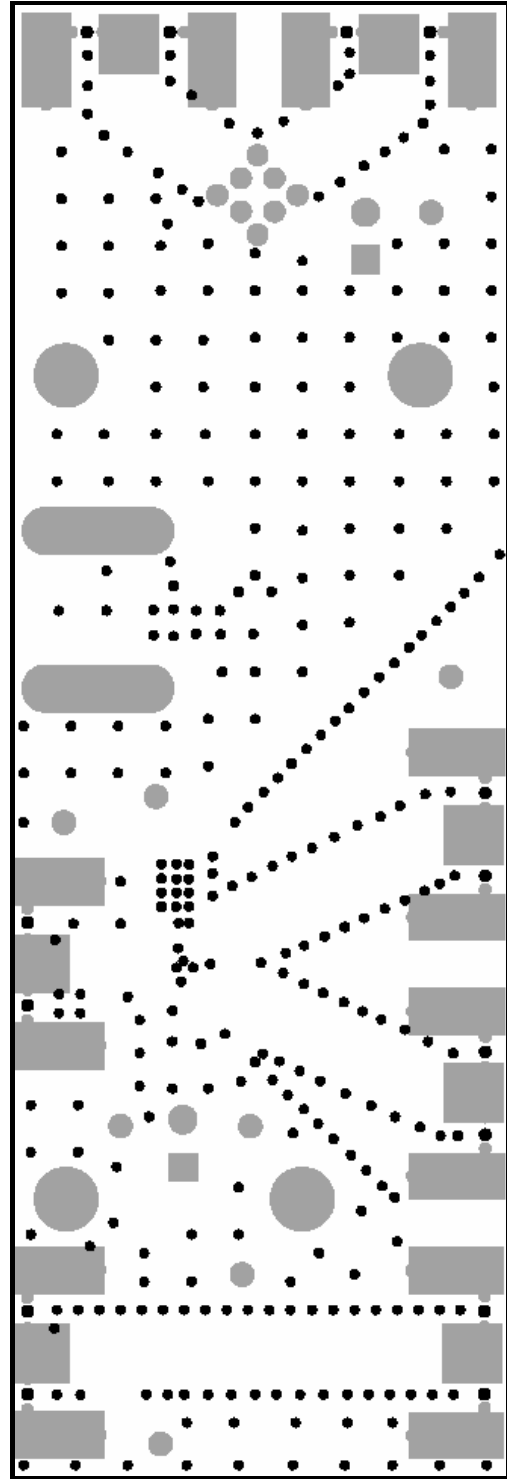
MAX3793 评估板 PC 板布局 - 焊接层
